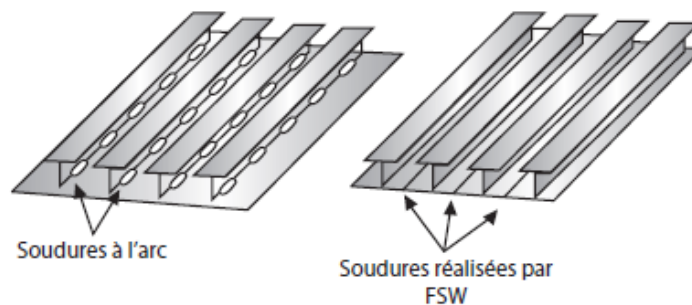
Structure soudée à l'arc et par friction malaxage [1]
